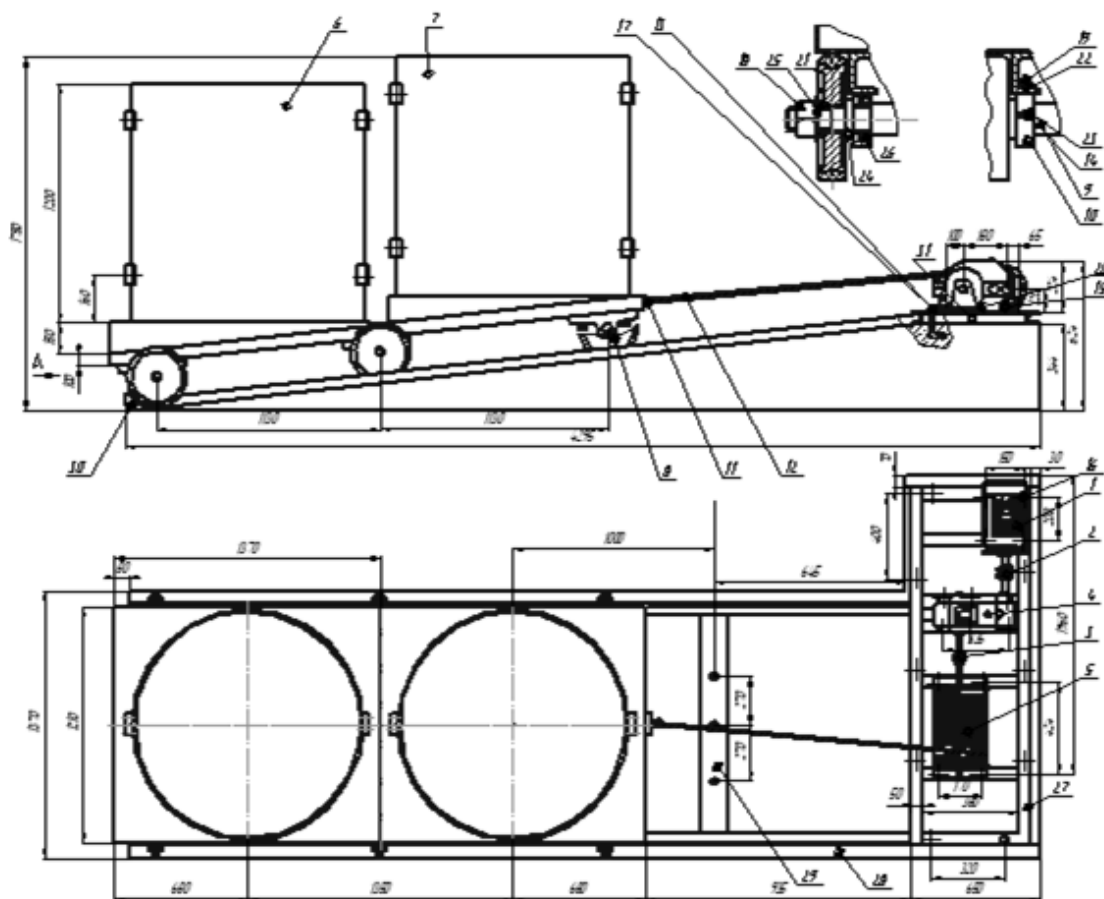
Тележка с механическим приводом: 1 – электродвигатель; 2 – муфта; 3 – муфта; 4 – редуктор цилиндрический; 5 – барабан; 6 – цилиндр нижний; 7 – цилиндр верхний; 8 – колесо; 9 – ось; 10 – обойма подшипника; 11 – фаркоп; 12 – трос; 13 – болт анкерный; 14 - 16 – болты; 17, - 20 – гайки; 21 – 25 – шайбы; 26 – подшипник; 27 – 29, 31 – швеллеры; 30 – откат
